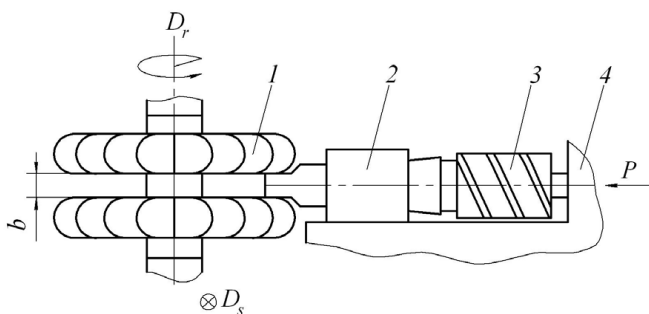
Схема фрезерования лапки двумя фрезами: 1 – фреза; 2 – зажимное приспособление; 3 – заготовка; 4 – упор
